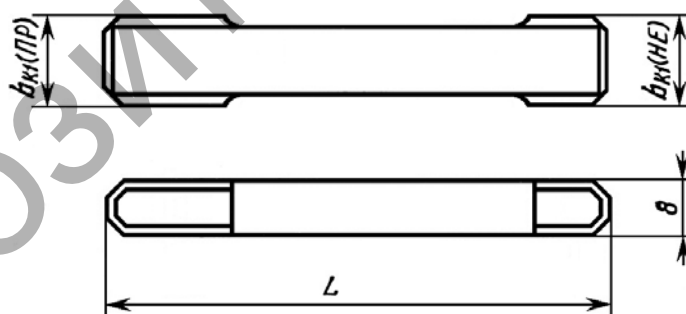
Пазовый калибр для контроля ширины пазов на валах и втулках
